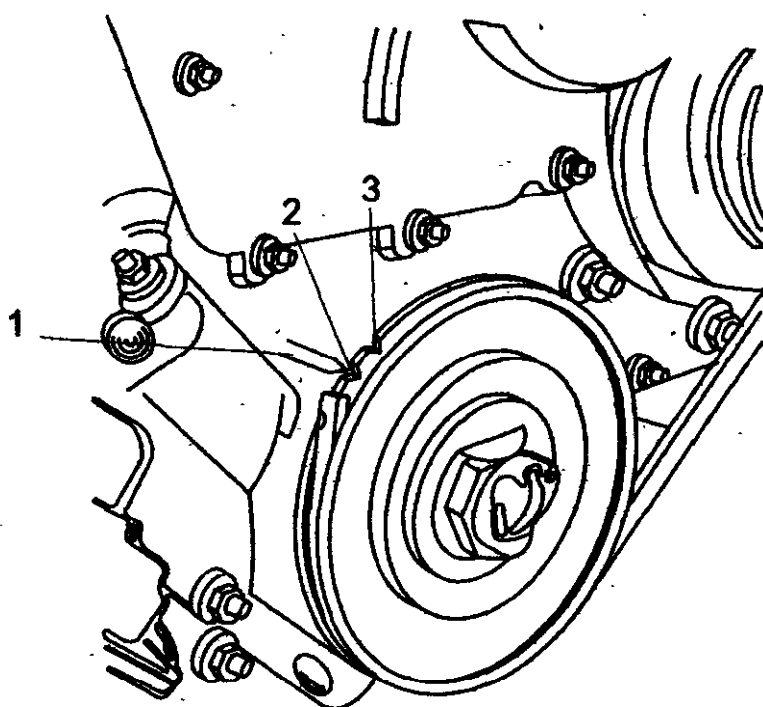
Положение установочных меток на шкиве коленчатого вала двигателя в момент нахождения поршня первого цилиндра в ВМТ:
